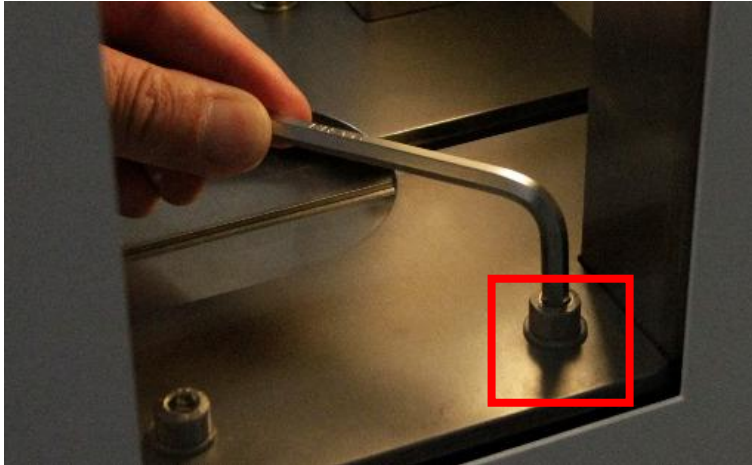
Soltar / retirar los tornillos en la cámara de compresión
